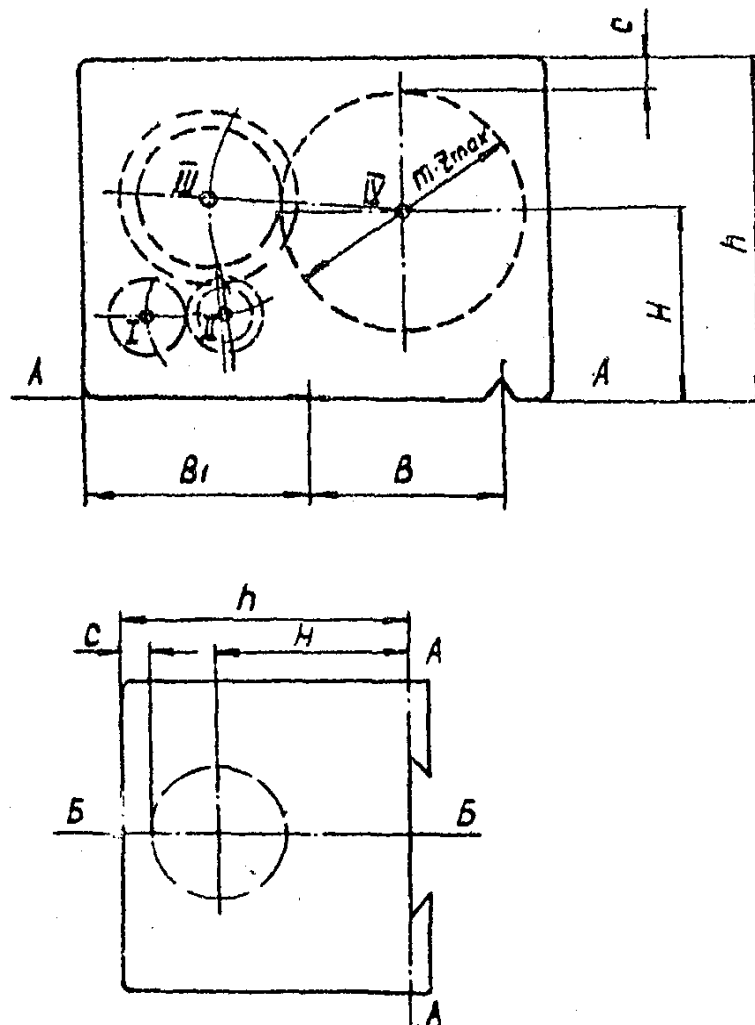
Свертка коробки скоростей токарно-винторезного станка
